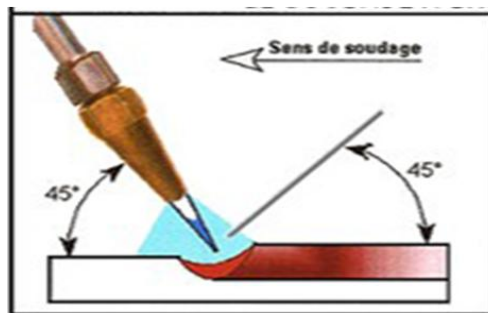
Le soudage à droite /en arrière [11].
